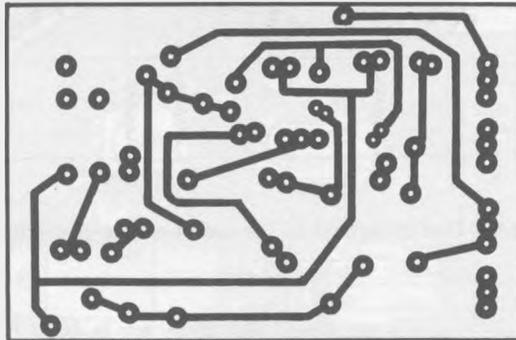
La plaquette de circuit imprimé, vue côté cuivre.
